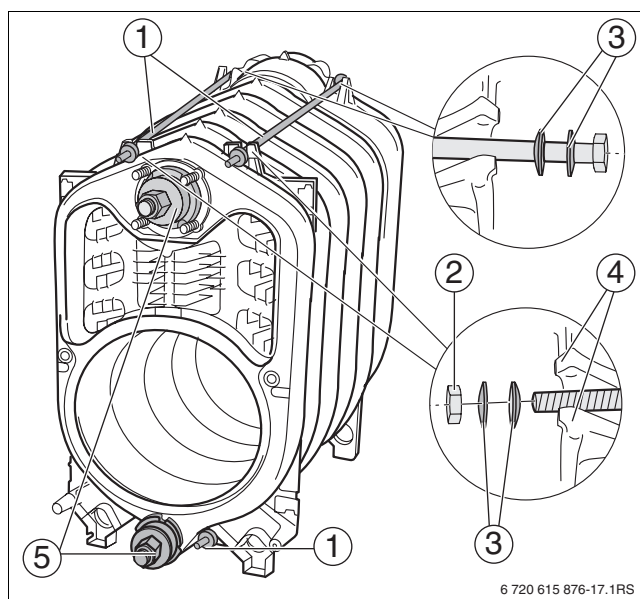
Montage des tiges d'ancrage – Disposition des ressorts à disque
